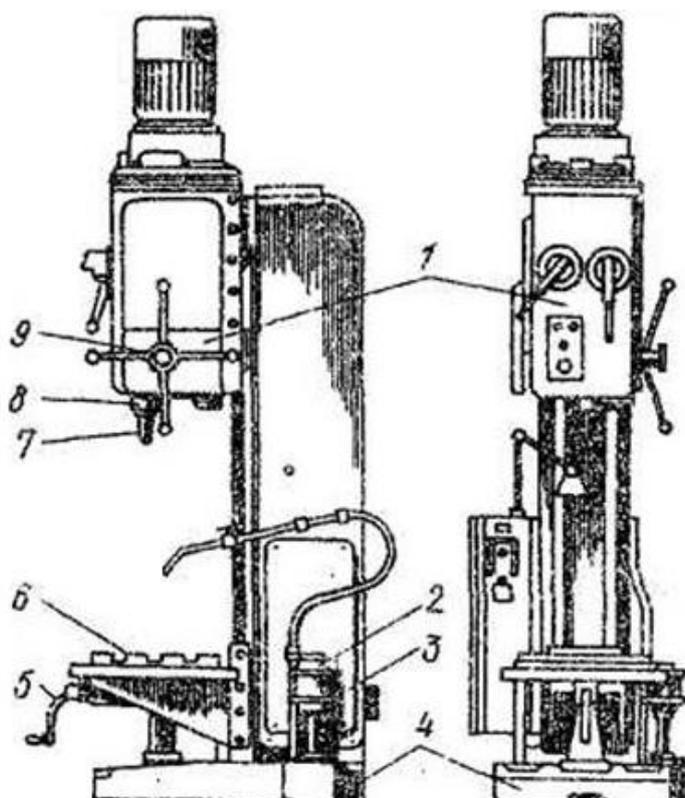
Одношпиндельный вертикально-сверлильный станок модели 2Н135
